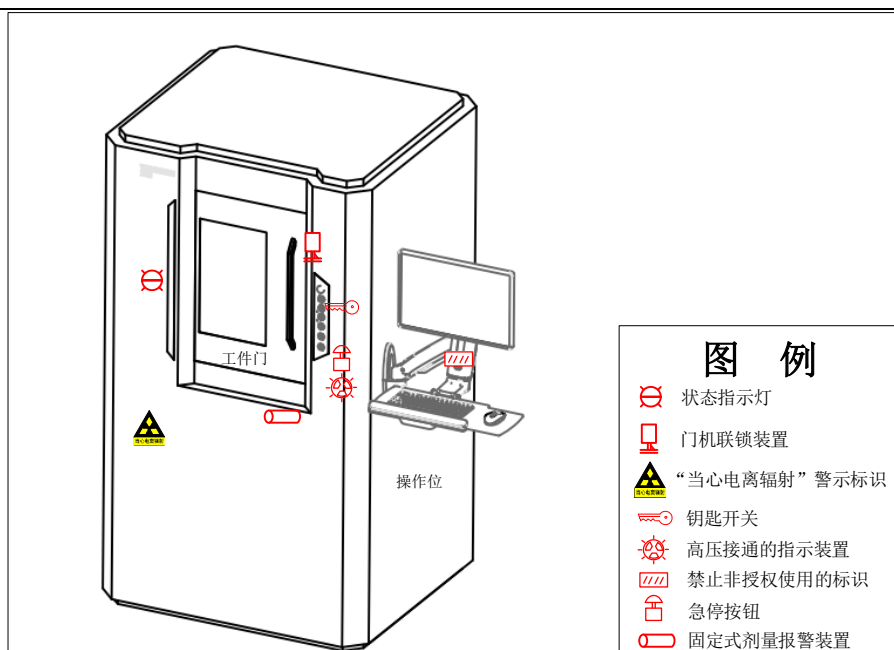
WX-DR-160E 型 X 射线探伤装置辐射安全措施布置示意图
